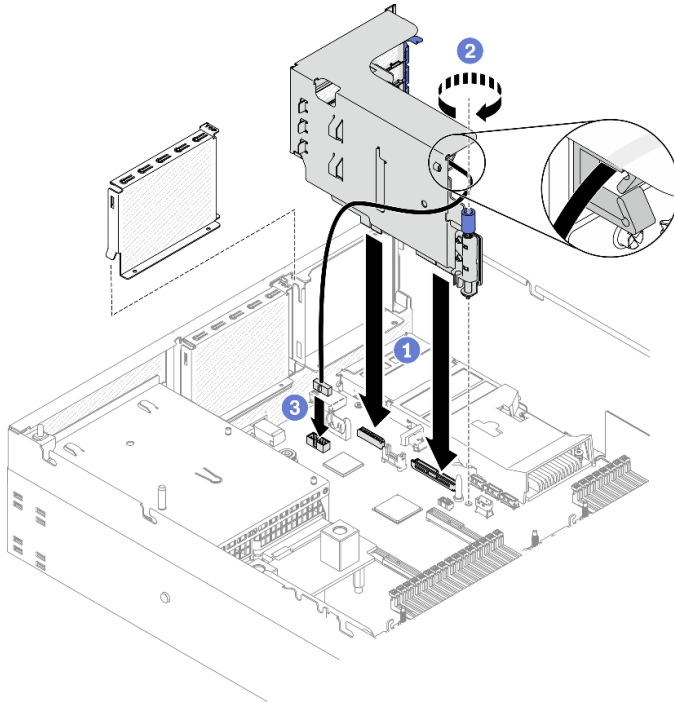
Instalando a placa riser PCIe 1 instalada com porta serial
